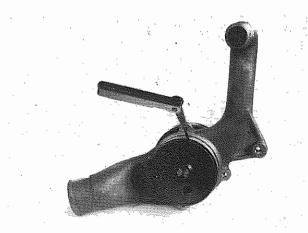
Gioco corpo e girante  $0.9 \pm 0.2$  mm Play between impeller and body  $0.9 \pm 0.2$  mm
